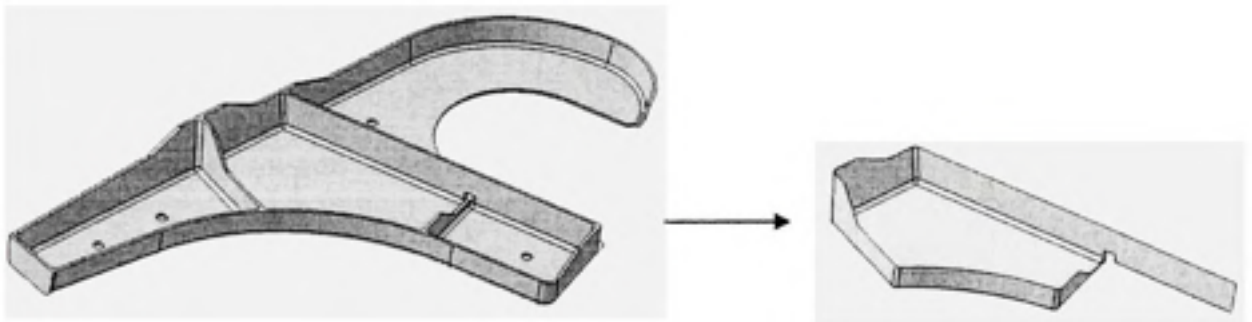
CF – Ensemble de faces dépendantes lors de l'usinage
